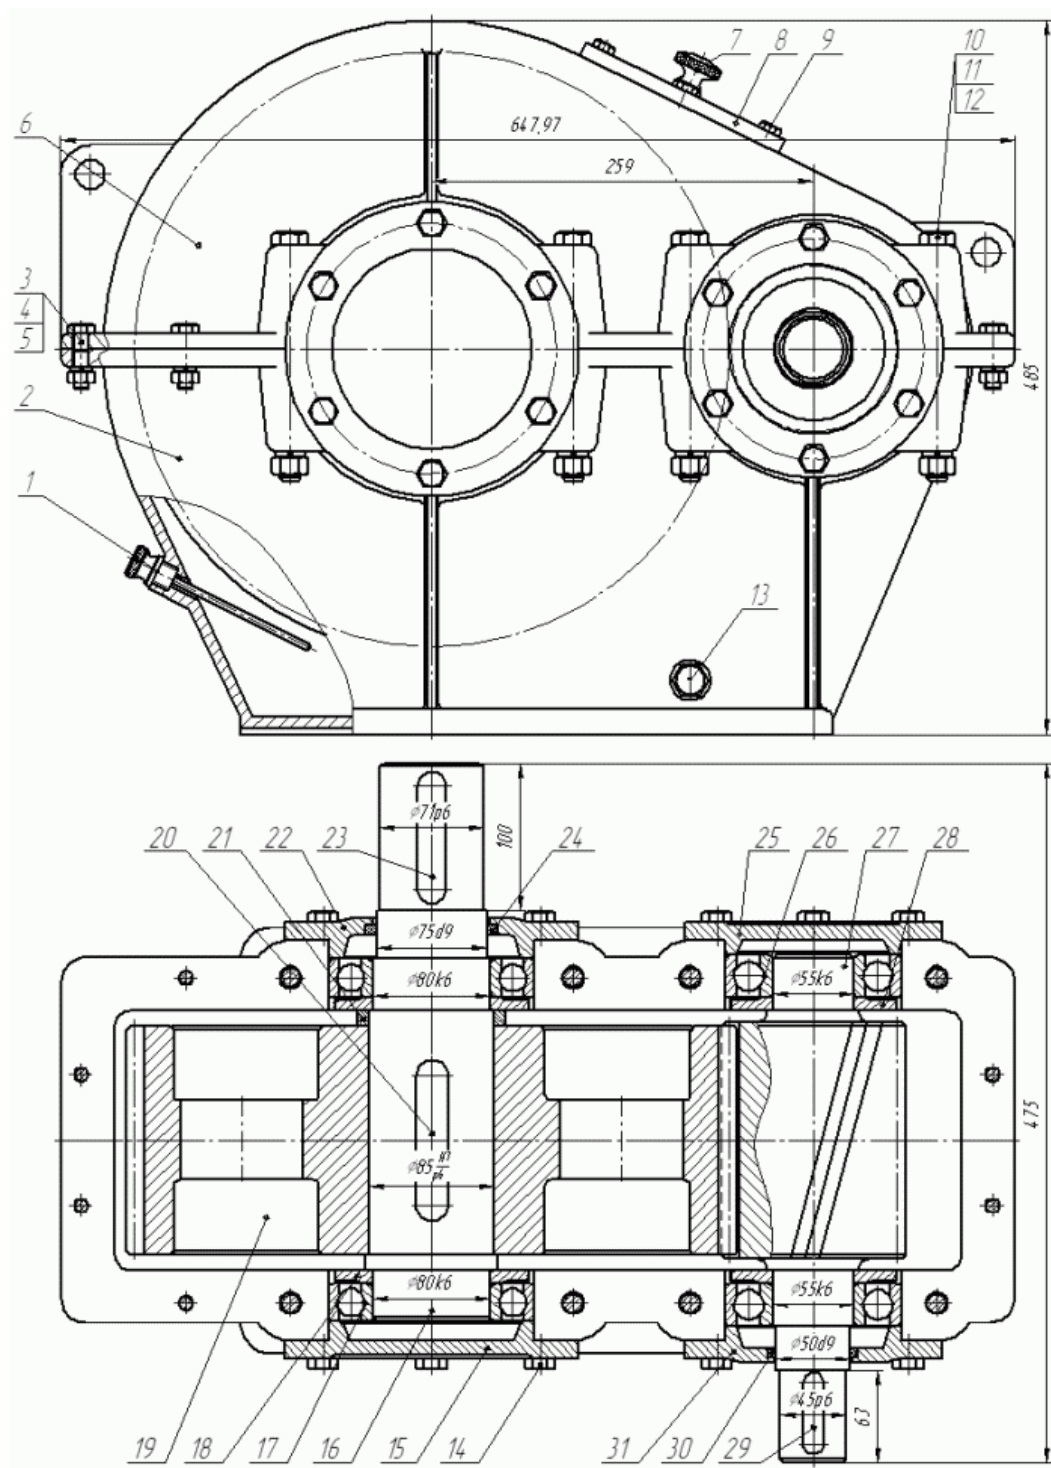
Цилиндрический одноступенчатый редуктор
